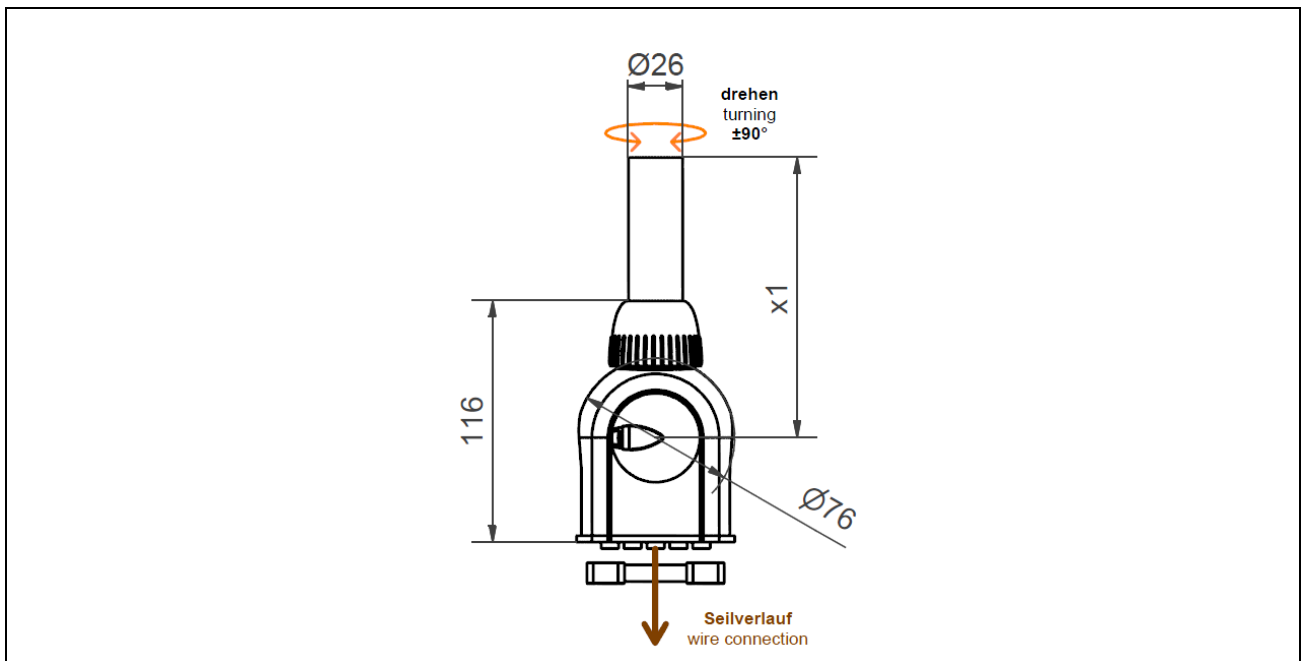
Maßzeichnung Drehgelenk RL-50-TL1
